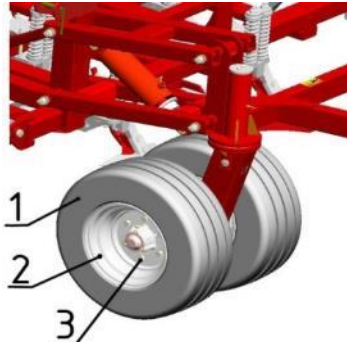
Опорно-транспортні колеса центральної рами культиваторної частини: 1 – шина; 2 – диск; 3 – болт.
